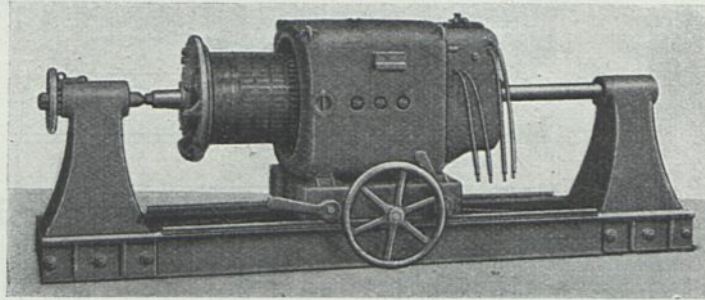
Spindelstock zum Herausnehmen des Ankers aus einem Motor mit einteiligem Kastengehäuse.
